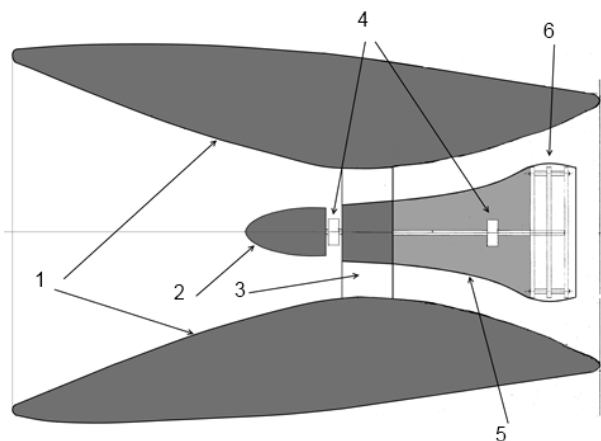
Схема ВЭУ и расположение узлов: 1 – концентратор (конфузор); 2 – носовой обтекатель; 3 – турбина; 4 – подшипники турбины; 5 – обтекатель генератора; 6 – генератор
